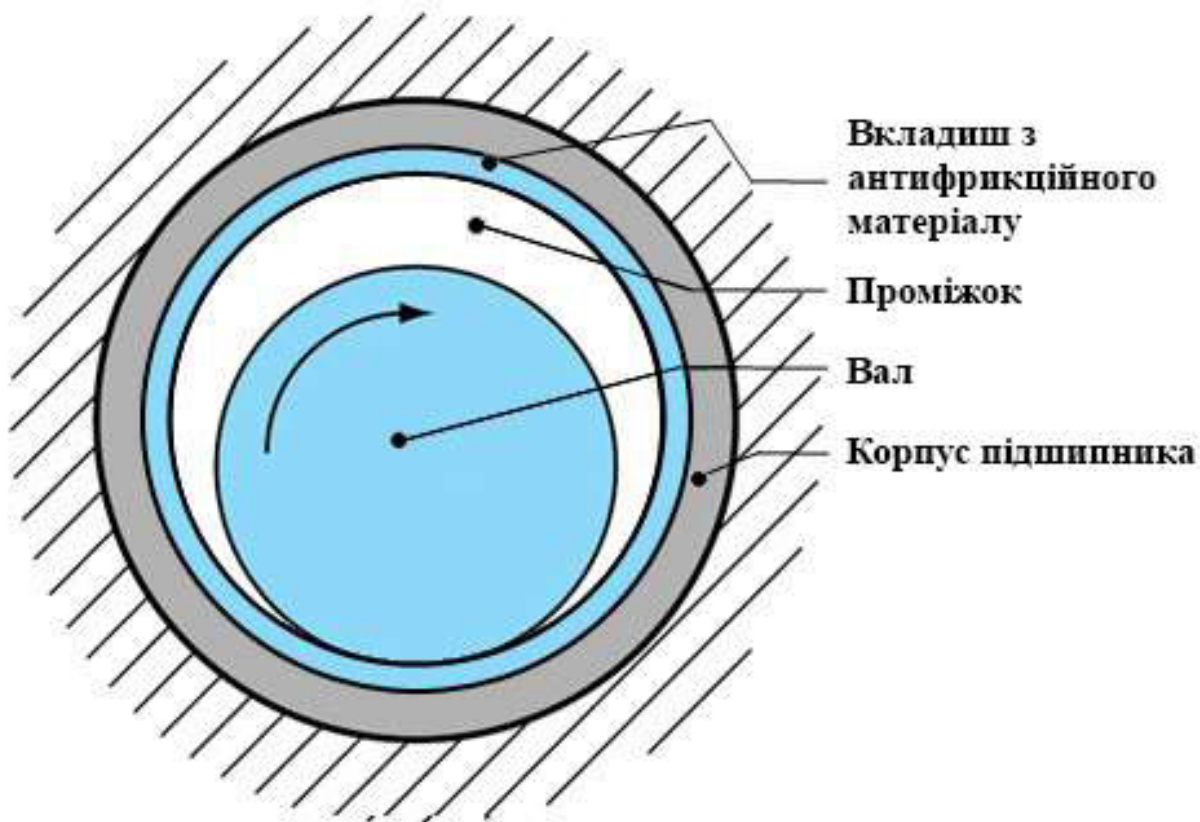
Принципова схема опори з підшипником ковзання
